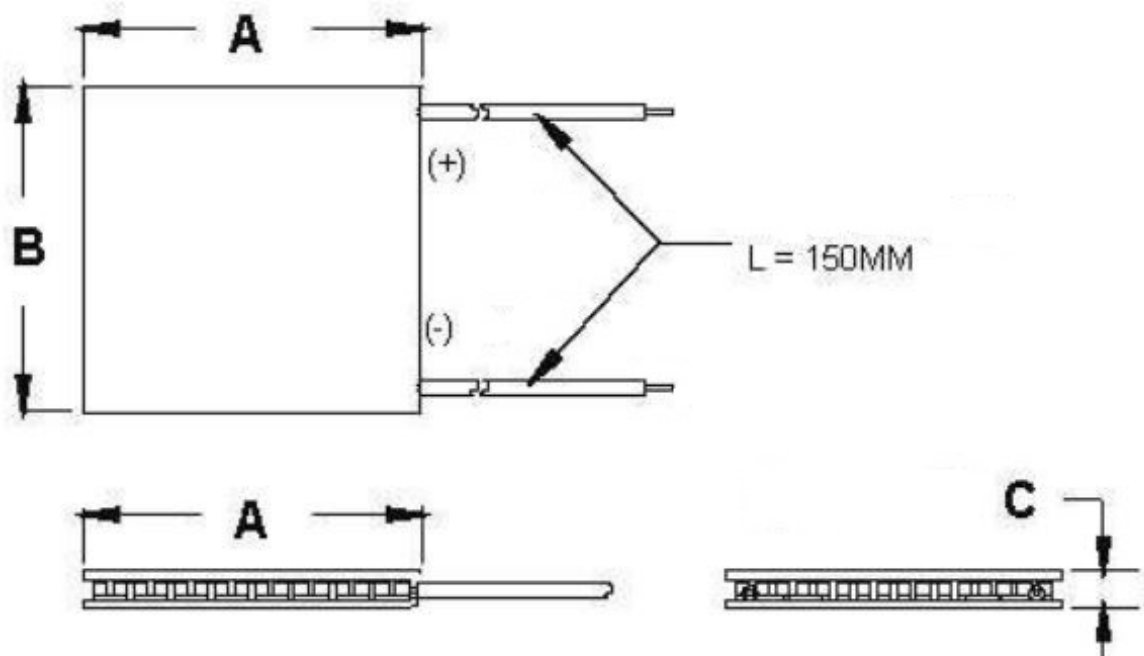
Габаритне креслення модуля TEC1-12712.
